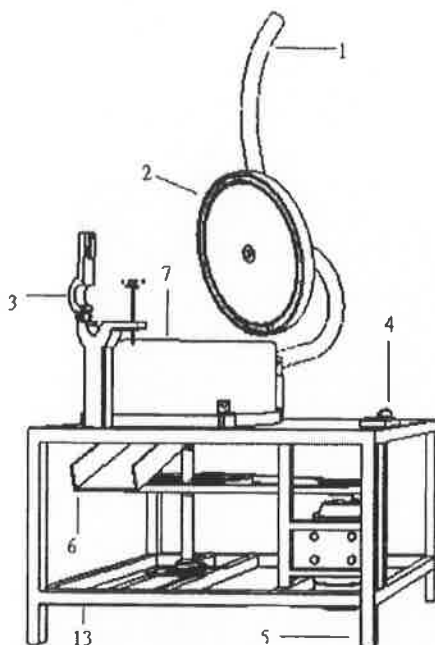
แบบเครื่องแยกผลปาล์มจากทะลายปาล์มน้ำมัน
